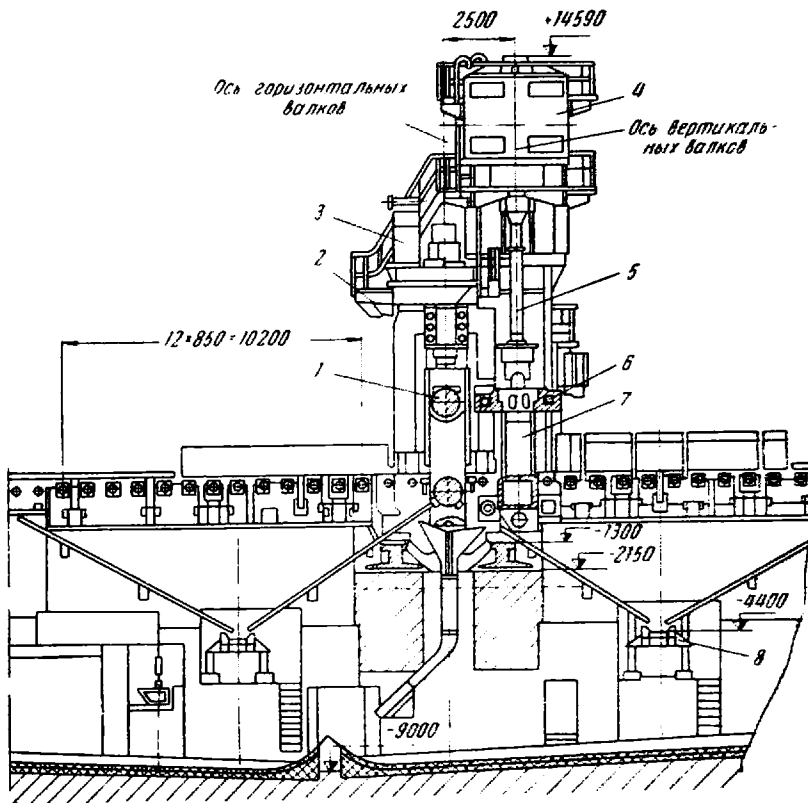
Общий вид рабочей клетки слябинга 1150:
